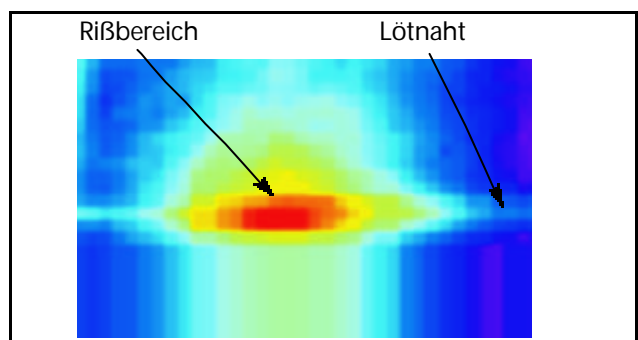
Wärmebild einer Lötnaht mit verdecktem Riß
